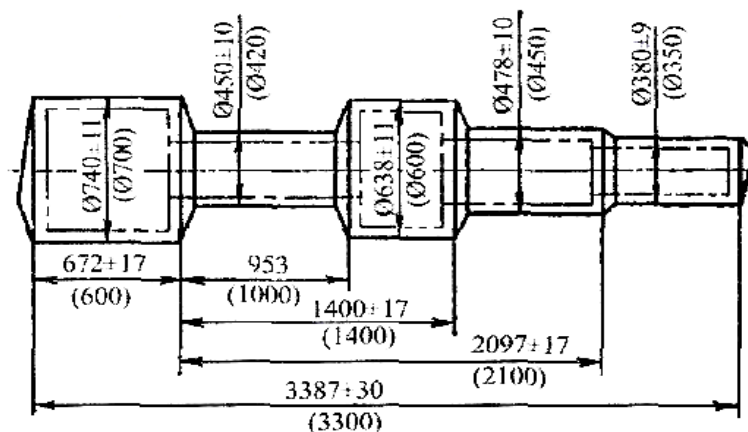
Чертёж поковки вала, полученный ковкой на гидравлическом прессе.
